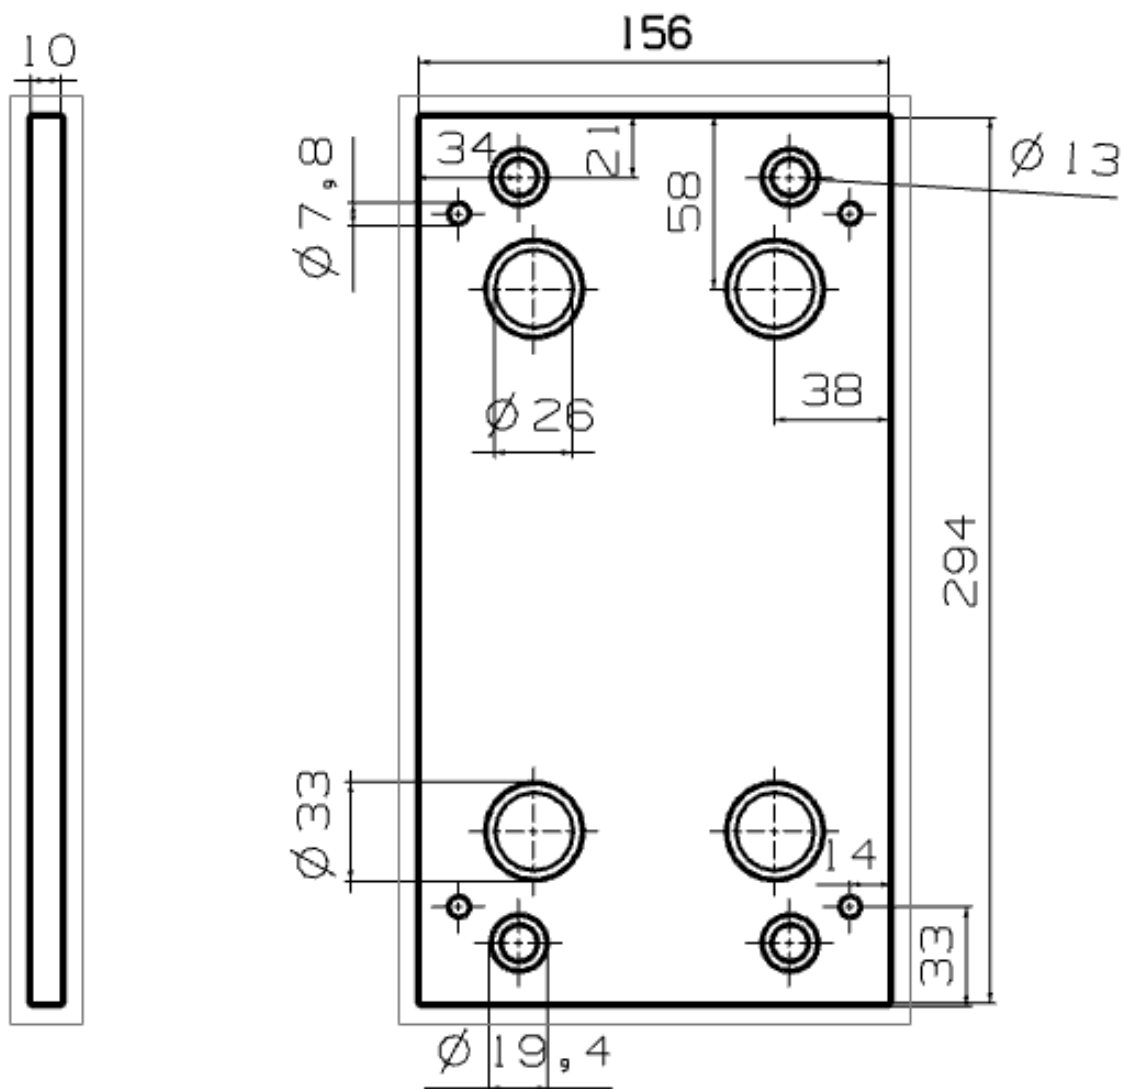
Descripción, placa limitadora de botadores CPE
